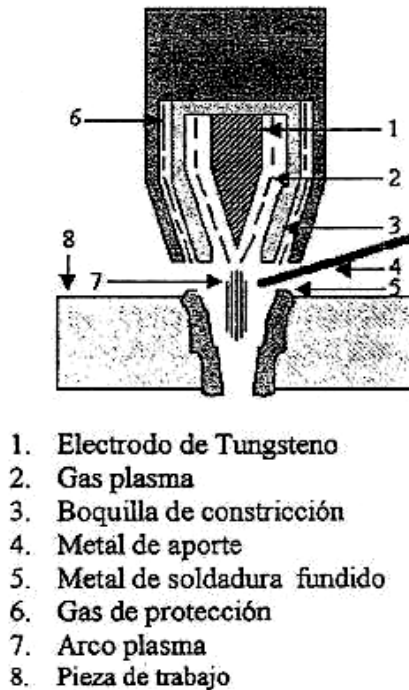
SOLDADURA POR ARCO PLASMA
